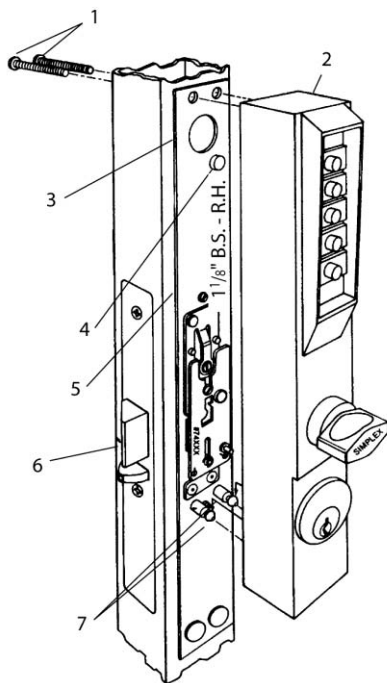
Крепление замка Simplex серии 3000 к обвязке: 1 — монтажные винты блока верхнего привода, деталь #54247 (2 шт.); 2 — корпус кодового замка; 3 — приводной блок (левостороннее приводное устройство, детали #74422 и #74418; правостороннее приводное устройство, детали #74420 и #74420); 4 — позиционирующая деталь корпуса; 5 — приводной блок #74XXX; 6 — защелка (направление защелки будет изменяться в зависимости от типа двери, здесь показана дверь, открывающаяся наружу); 7 — монтажные стойки (С разрешения компании Simplex Access Controls Corp.)
